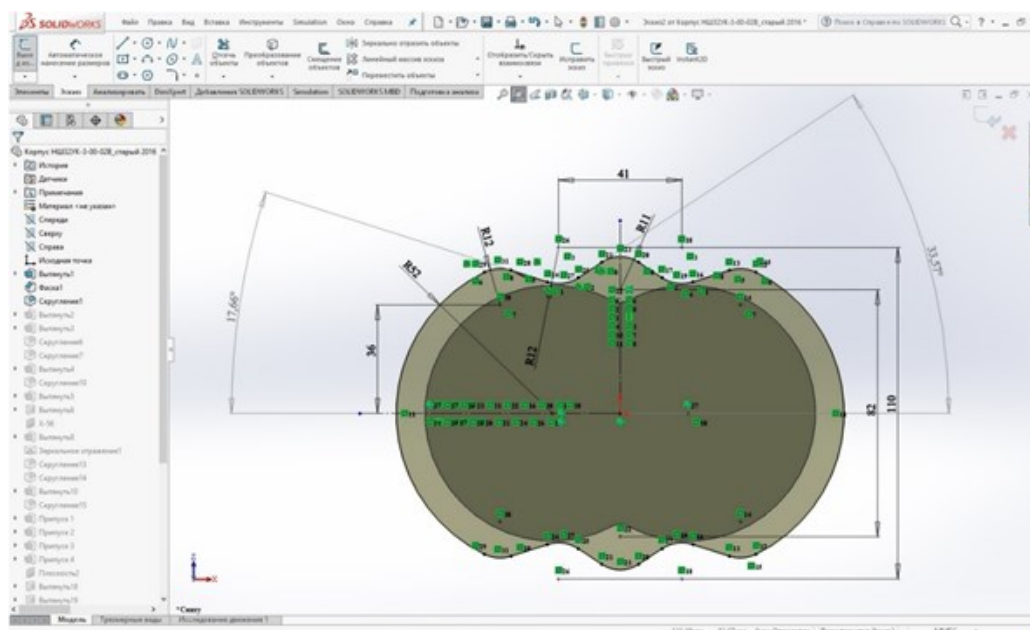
Побудова ескізу нижньої частини виливка
